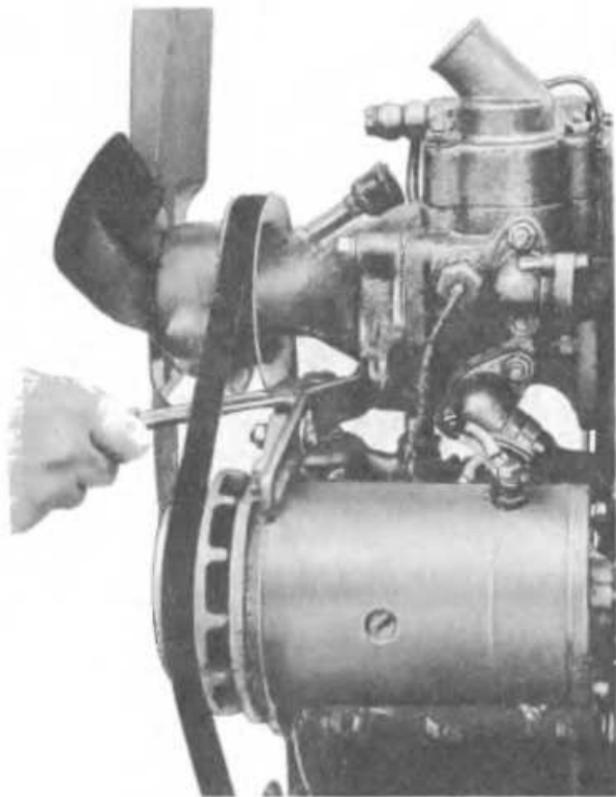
Проворачивание стержня фильтра грубой очистки одно- и двухцилиндровых дизелей
